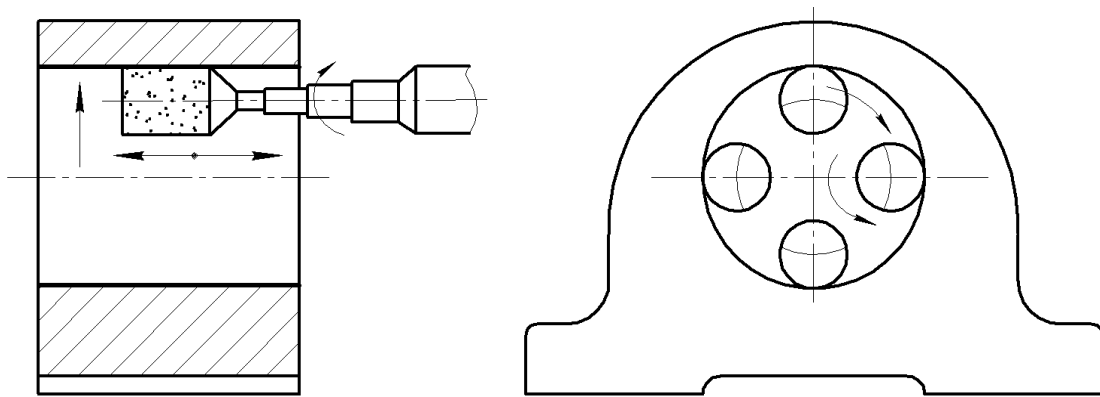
Схема шліфування корпусу на планетарно-шліфувальному верстаті
